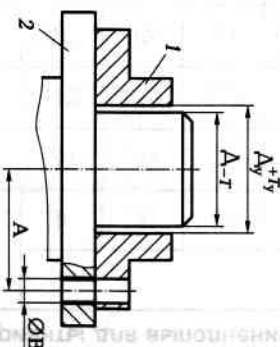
Схема установки заготовки при обработке плоского хвостовика
